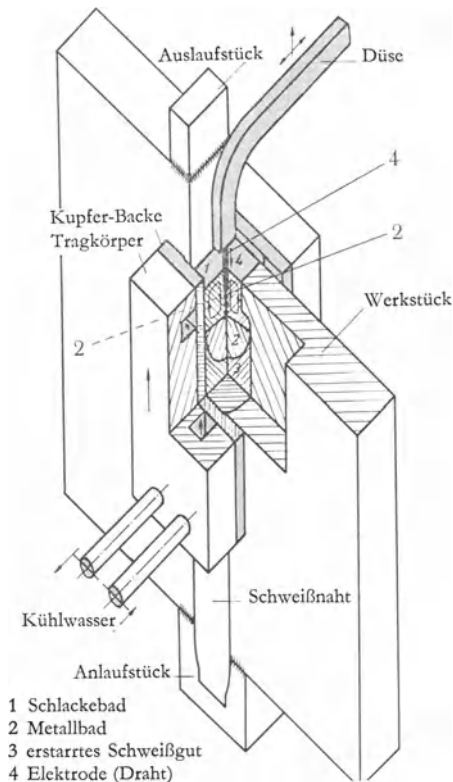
Arbeitsablauf beim Elektro-Schlacke-Schweißen (ESS)
